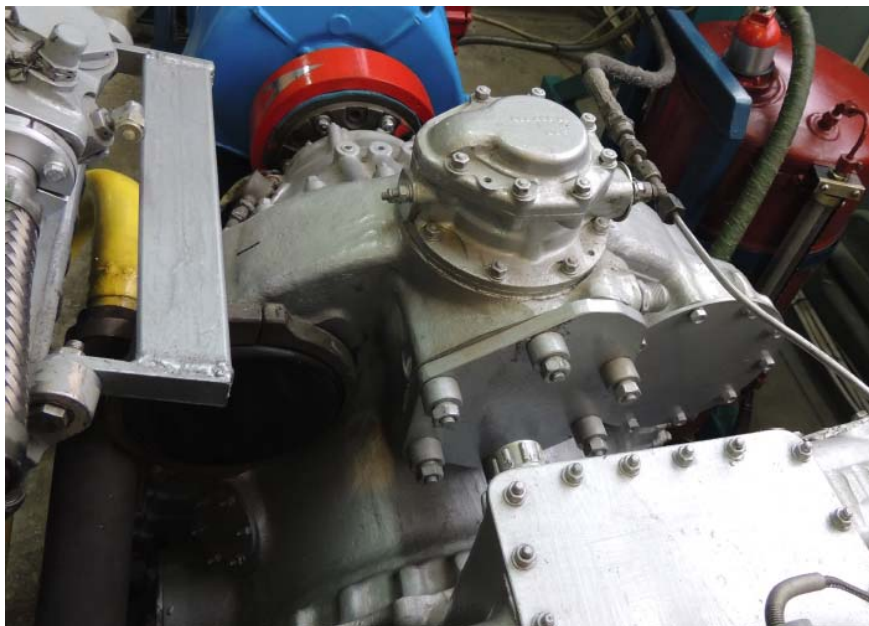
Заглушки на фланцях агрегатів лобового картера
